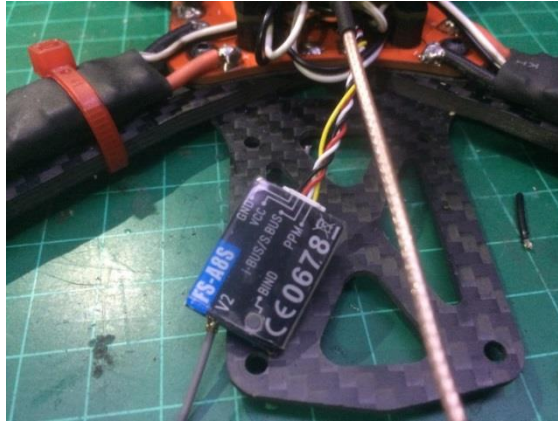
15: Montaje receptor de control RC Flysky FS-i6.
